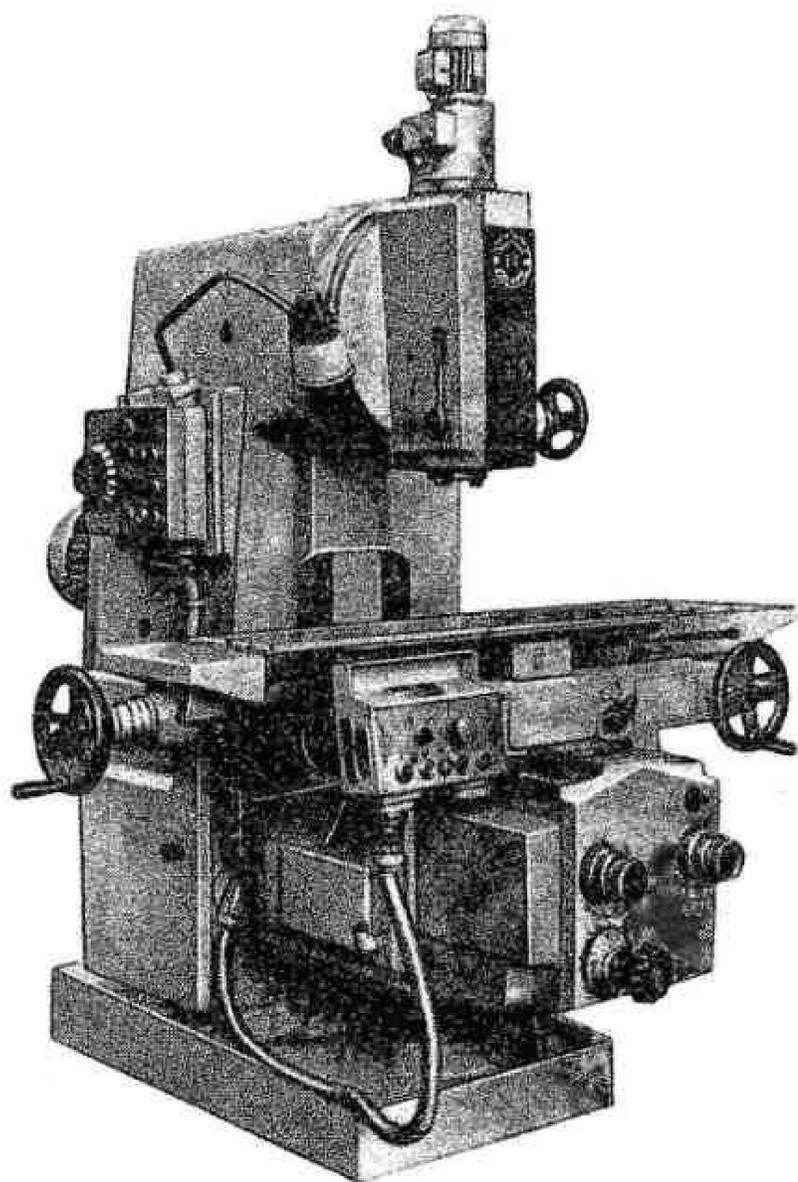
Вертикальный консольно-фрезерный станок 6Т12-1
